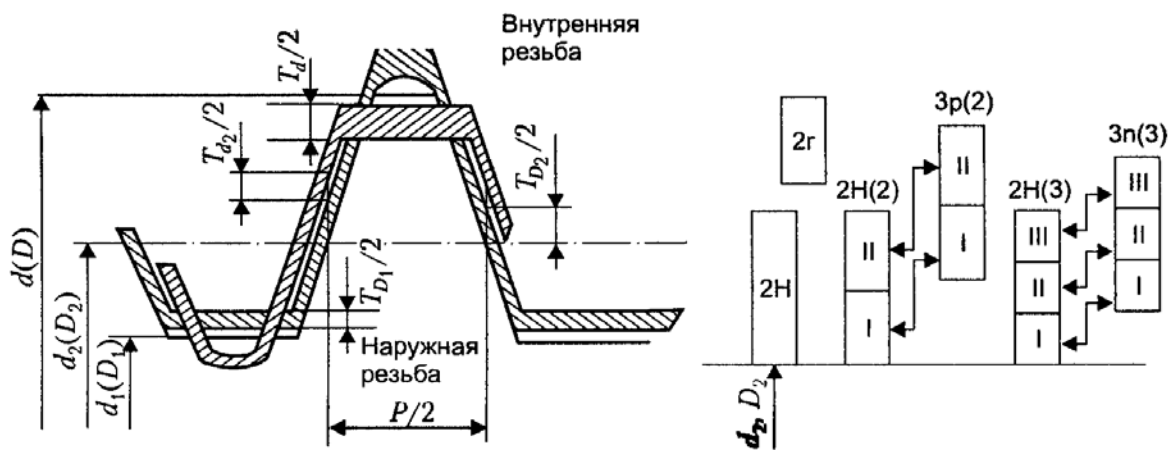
Расположение полей допусков резьбы с натягом
